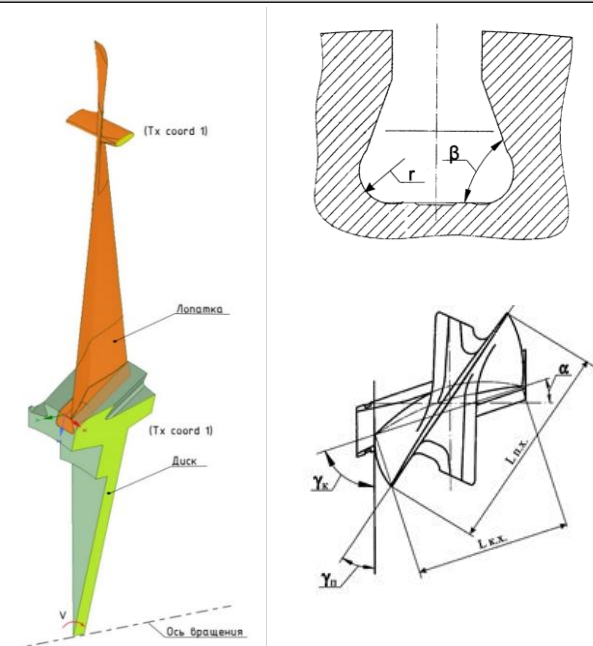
Геометрическая модель рабочего колеса компрессора газотурбинного двигателя
